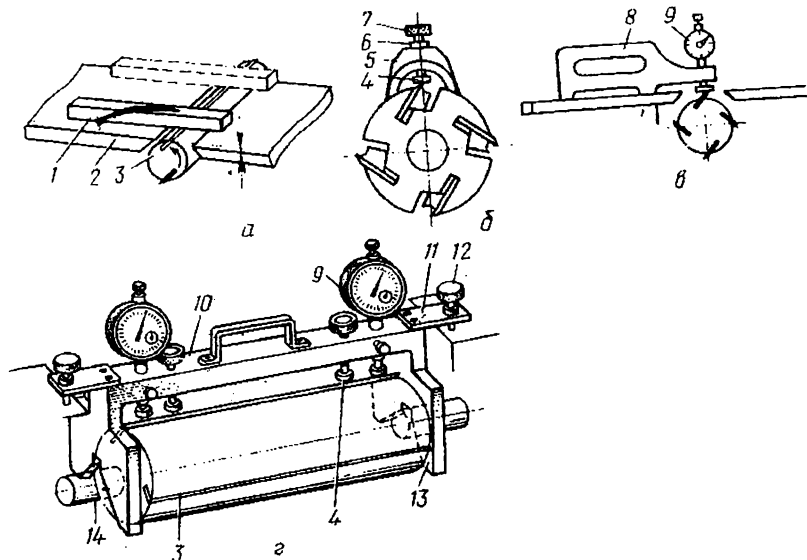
Контрольно-установочные приспособления для выверки ножей в ножевых валах: а - контрольной линейкой или бруском; б - шаблоном; в - индикаторным прибором, установленным на столе; г - индикаторным прибором с базированием на подшипниковых шейках вала; 1 - брусок (линейка); 2 - стол; 3 - ножевой вал; 4 - упор; 5 - скоба; 6 - контргайка; 7 - винт; 8 - основание; 9 - индикатор; 10 - корпус; 11 - пластинчатая пружина; 12 - винт крепления; 13 - базирующий элемент; 14 - шейка ножевого вала
